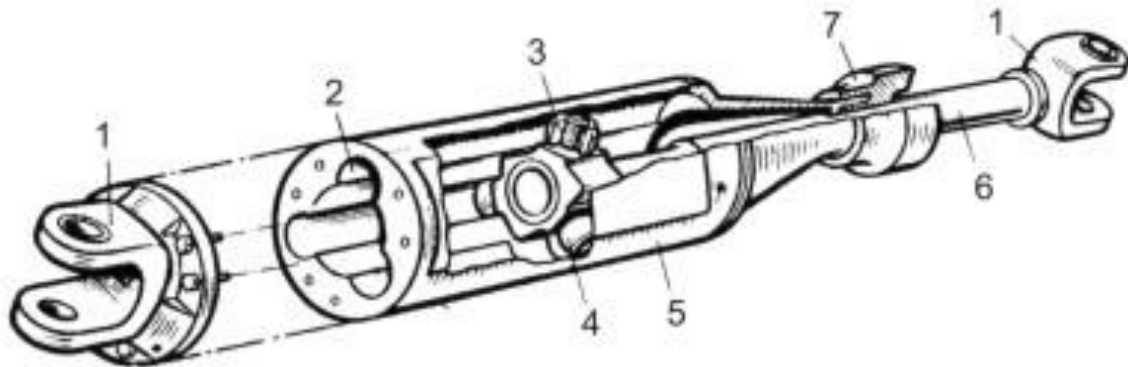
Тягова муфта "Трипод": 1 – з'єднання із шарніром Гука; 2 - циліндричний паз; 3 - голчастий підшипник; 4 - сферичний ролик; 5 - корпус муфти; 6 - ведений вал муфти; 7 - ущільнення рухомого вала.
